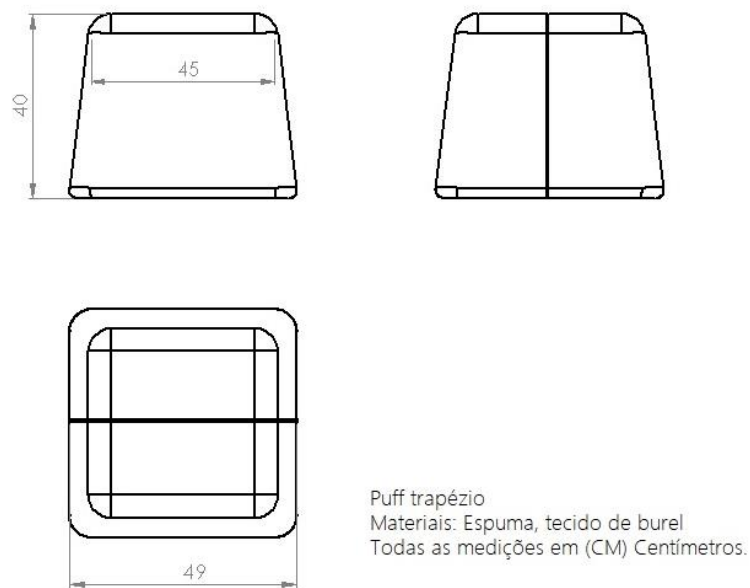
Desenho técnico CAD 3D do conceito Trapézio (Fonte: Autor)
